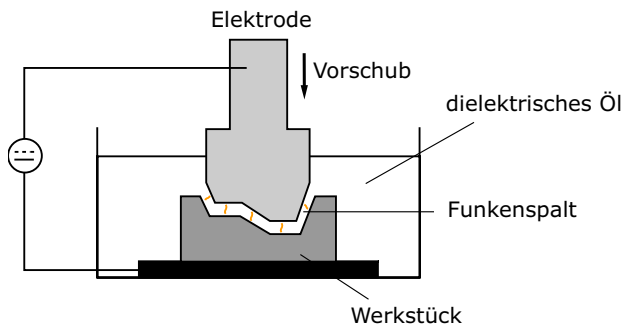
reZ) Funktionsprinzip einer Senkerodiermaschine mit Werkzeugelektrode, welche das Negativ des Werkstückes darstellt
